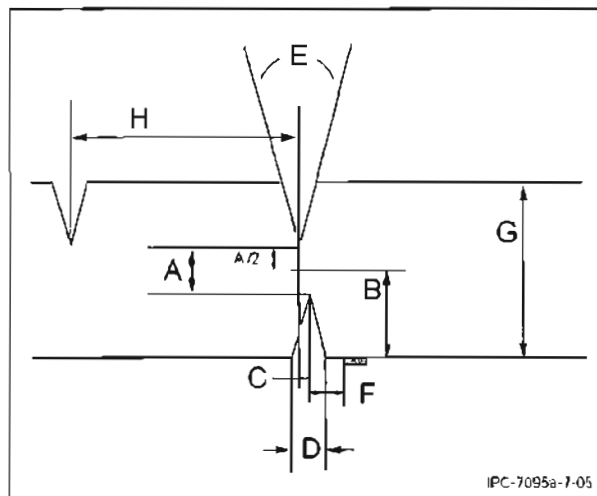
Стандартные параметры канавок для разделения заготовок
